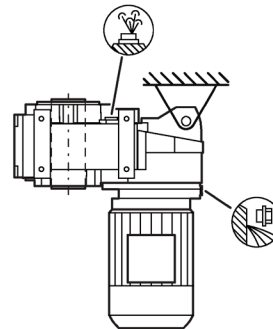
Einbaulagen für Stirnradgetriebe DF/ZF Flanschausführung, Baugrößen 49 - 189 und DZ/ZZ mit Gehäuseflansch, Baugrößen 49 - 129
